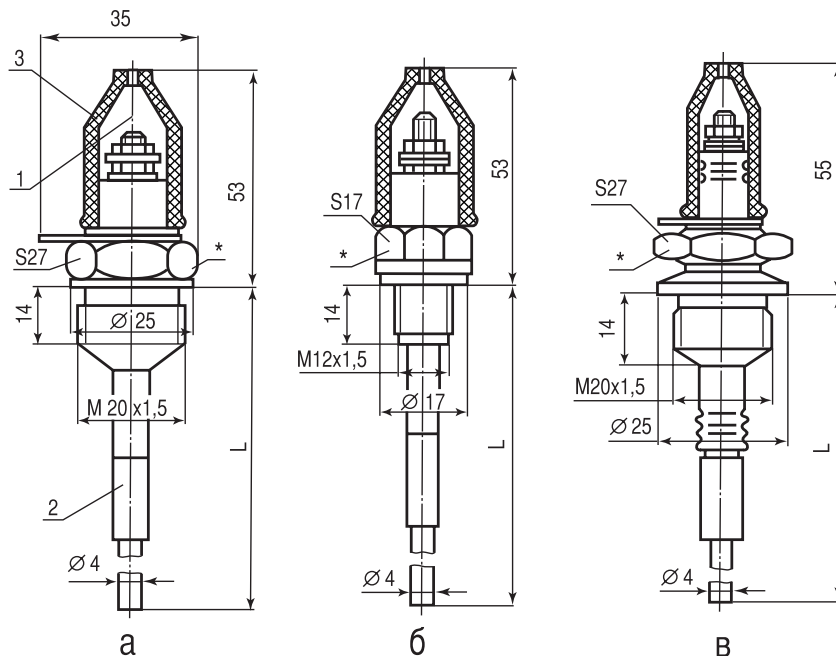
Габаритные и установочные размеры преобразователя передающего ППР
